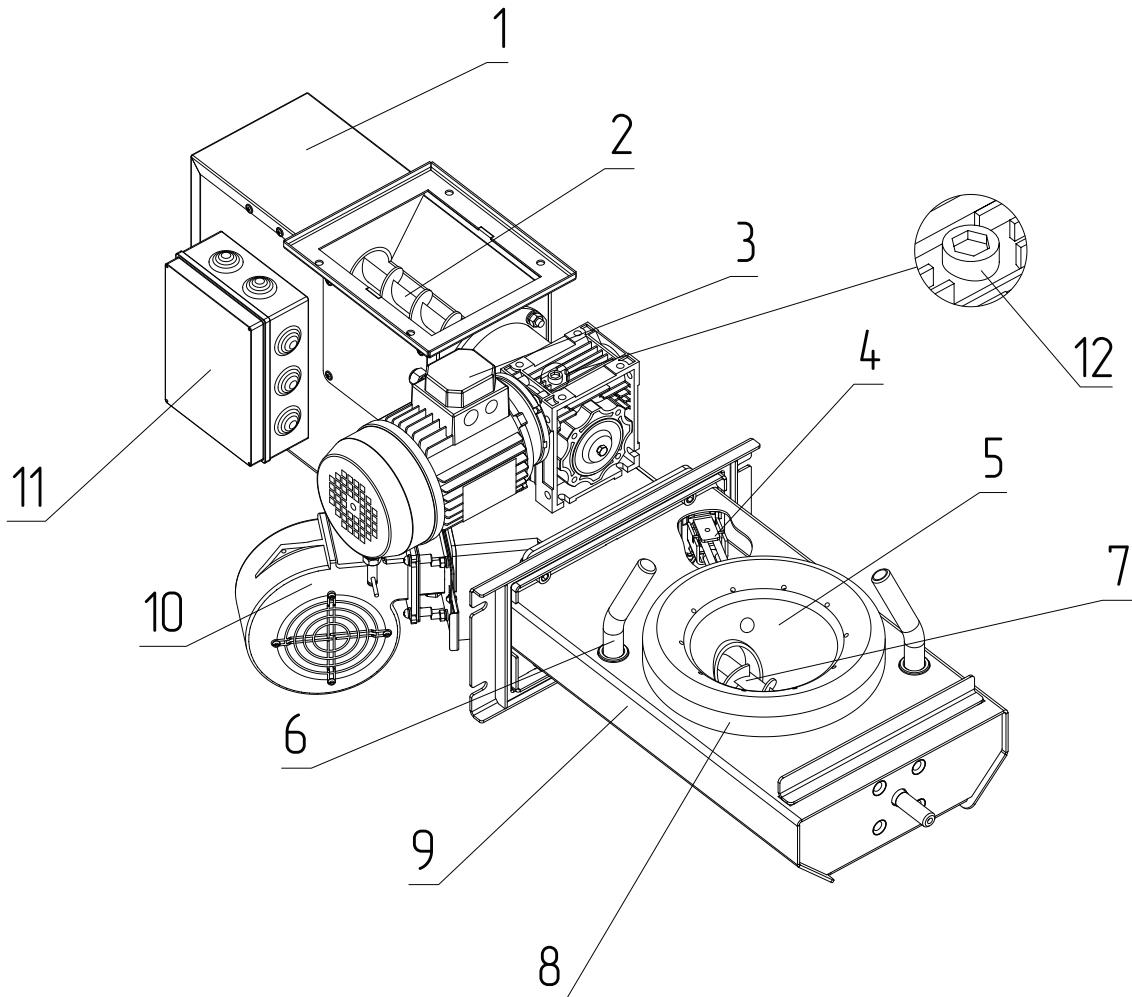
Пеллетная горелка котла ZOTA Pellet S с приводом
